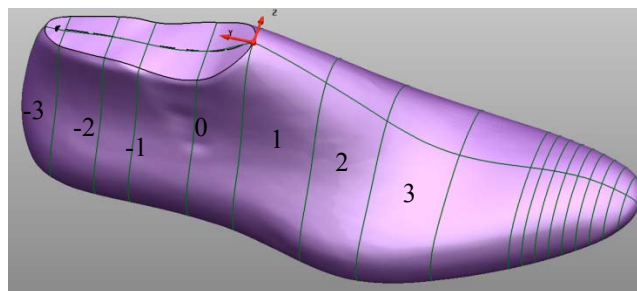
Побудова продольного та поперечно-вертикальних перерізів колодки
